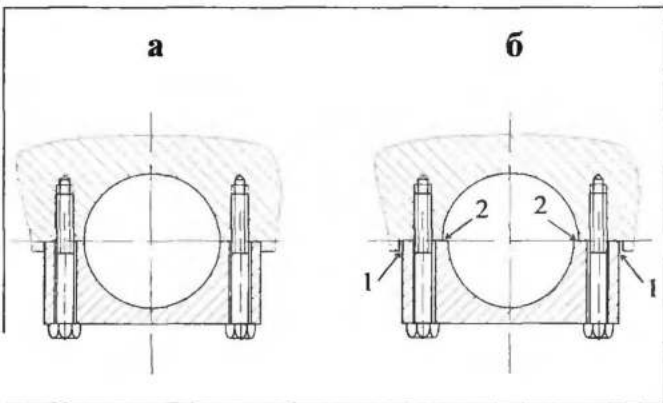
Схема деформации коренной крышки после перегрева подшипника:
